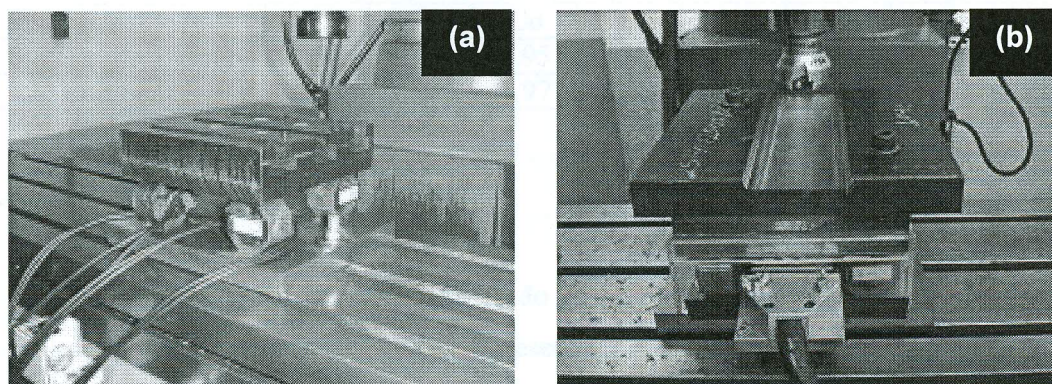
Mesa instrumentada utilizada para medir os esforços de usinagem (a) e equipamento montado para ensaio de fresamento (b).
